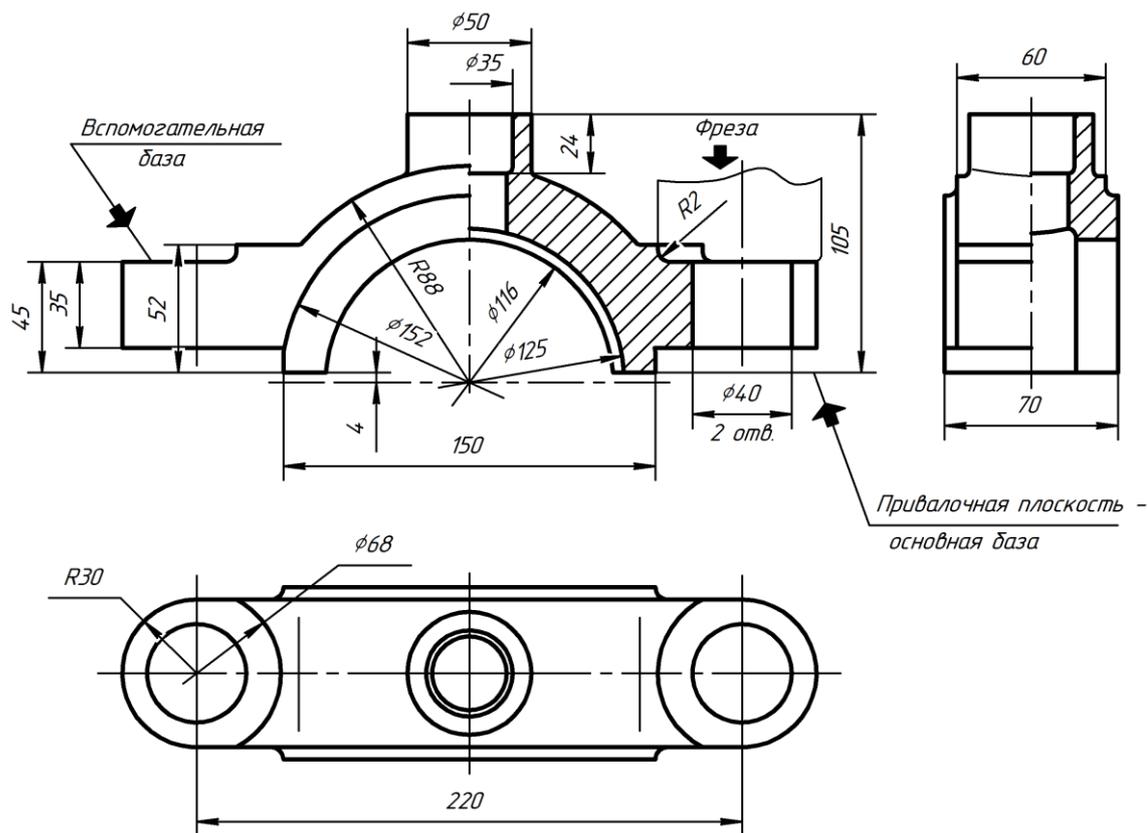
Размерные базы — плоскости (привалочные и др.) на примере типовой детали (крышка подшипника)
